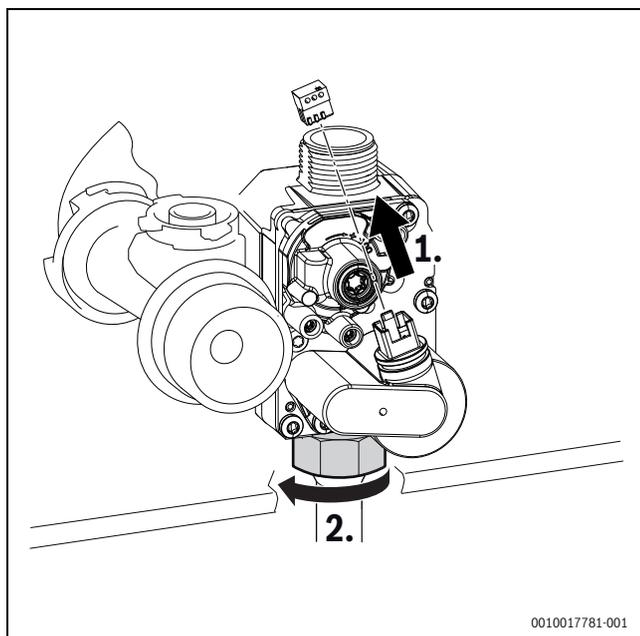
Retirer le connecteur et desserrer l'écrou-raccord
